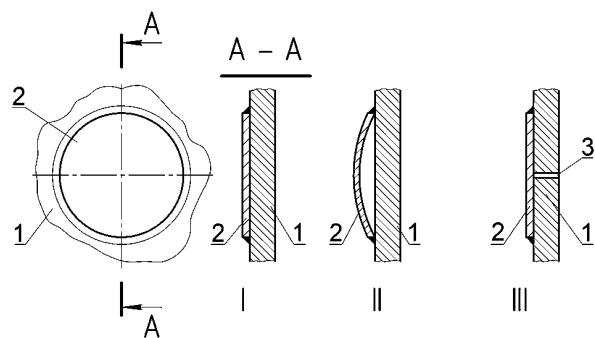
Пример неверной конструкции отбойника: 1 – корпус сосуда; 2 – отбойник; 3 – сварной шов; 4 – отверстие.
